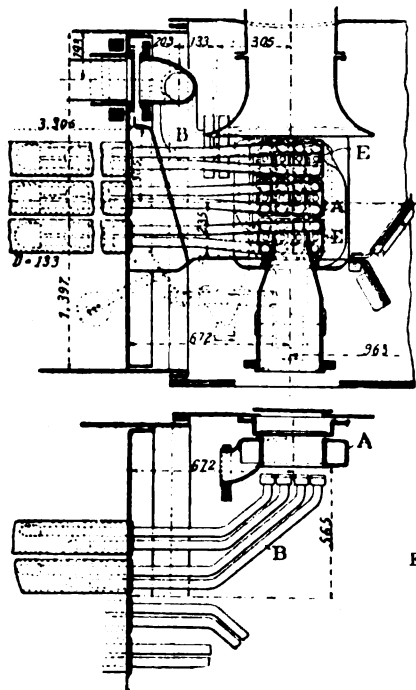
Surriscaldatore Cole. — Sezioni, pianta e vista dei collettori.
